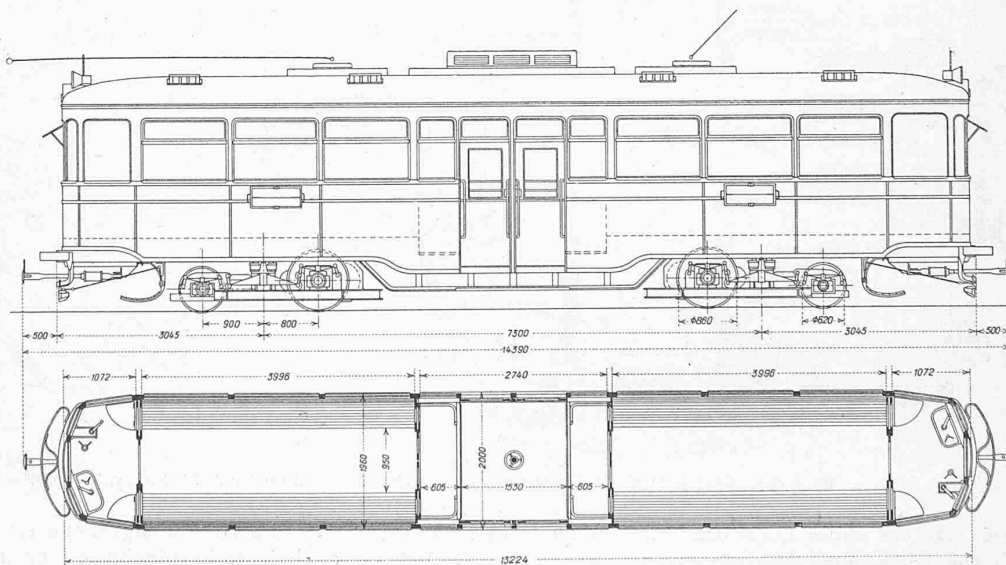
Elévation et plan de la voiture motrice à quatre essieux, avec entrée centrale. — Echelle de 1 : 100.
